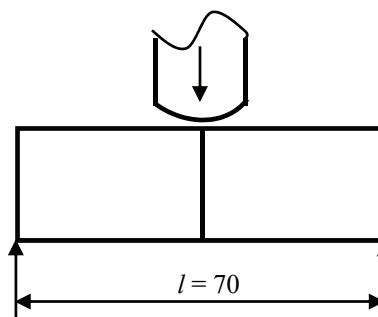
Схема испытаний на изгиб сварных образцов
